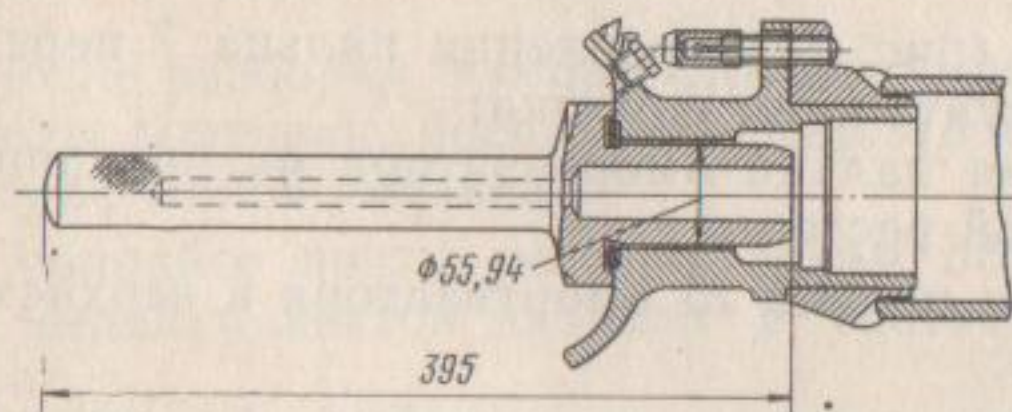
Оправка для запрессовки шаровой опоры в картер переднего моста
